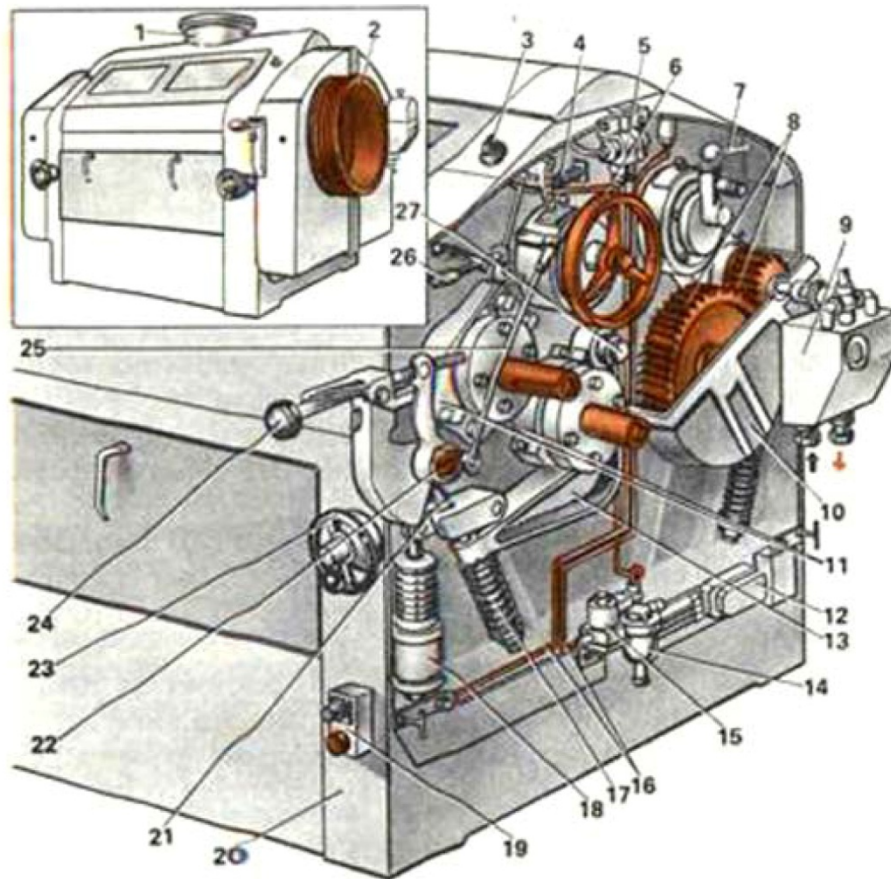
Вальцовий верстат А1 -БЗ-2Н:1 - горловина; 2 - шків; 3 – пневмоперемикач привалу-відвалу; 4 - пружина заслінки; 5 - перетворювач сигналу; 6 - шків живильного механізму; 7 - рукоятка перемикачання швидкостей; 8 - шестерні міжвальцьової передачі; 9 - корпус системи охолодження; 10 - кожух міжвальцьової передачі; 11 - корпус підшипника; 12 - блок реле; 13 – лікоть рухливого корпусу підшипника; 14 - фільтр повітряний; 15 - клапан електромагнітний; 16 - повітрепроводи; 17 - пружина запобіжна; 18 - пневмоциліндр; 19 - кнопки "Пуск", "Зупинка"; 20 - станина; 21 - підвіска; 22 - вал ексцентриковий; 23 - штурвал механізму налагодження паралельності вальців; 24 - рукоятка точного налагодження міжвальцьового зазору; 25 - тяга; 26 - гвинт обмежувальний; 27 - цапфа.
